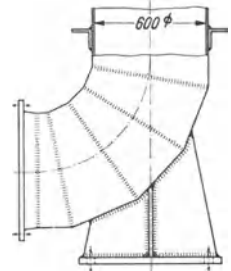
Geschweißter Segmentkrümmer.
